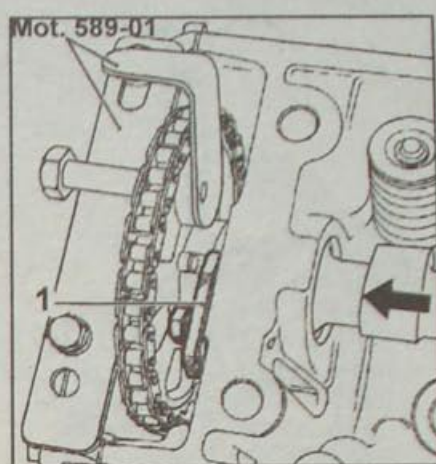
Расположение приспособления Mot. 589-01, упора (1) и направления перемещения распределительного вала
